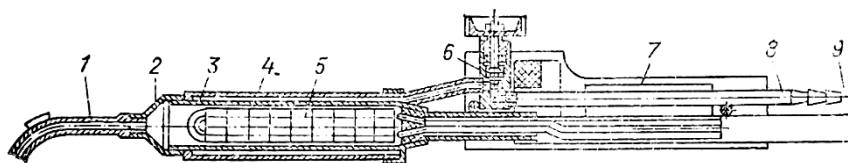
Горелка для сварки пластмасс:
